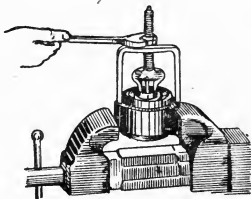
Съёмник для выпрессовки подшипников из корпусов.
